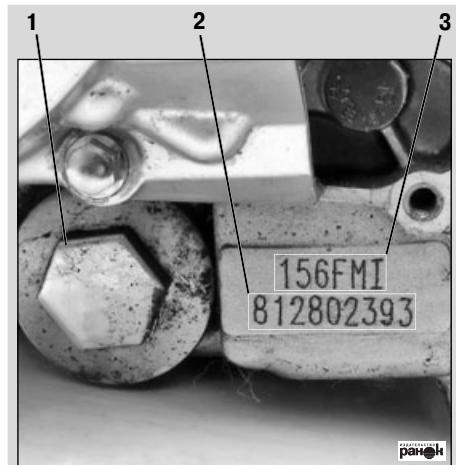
Расположение идентификационного номера двигателя: 1 – сливная пробка моторного масла; 2 – идентификационный номер двигателя; 3 – модель двигателя
